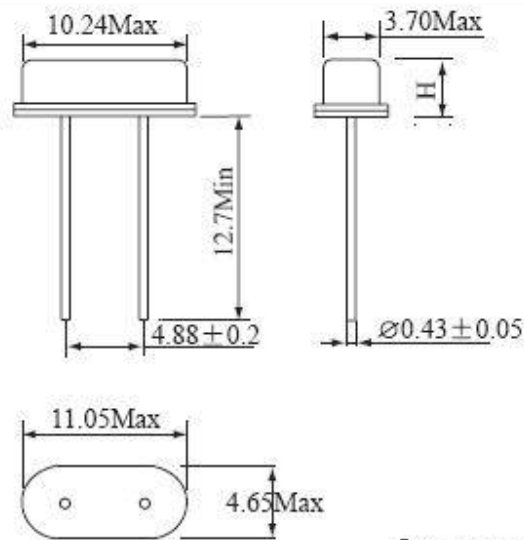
Габаритні розміри кварцевого резонатора НС-49U-16МГц
